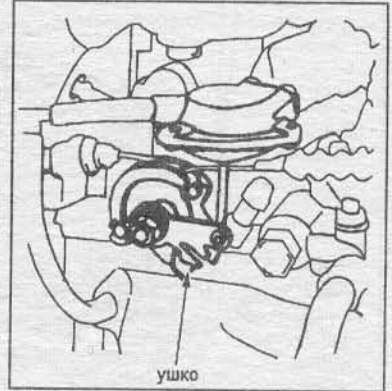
Регулировка оборотов двигателя подгибанием ушка рычага привода.
